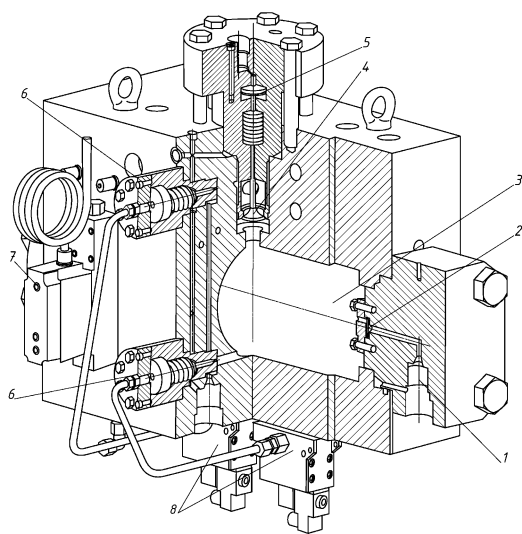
Модуль управления подачей газа двигателя серии ME-GI: 1 – узел ввода ГТ; 2 – обратный клапан; 3 – полость аккумулятора давления; 4 – главный отсечной клапан; 5 – поршень привода главного отсечного клапана; 6 – клапан продувки инертным газом; 7 – блок управления главным отсечным клапаном; 8 – блок управления клапаном продувки инертным газом
